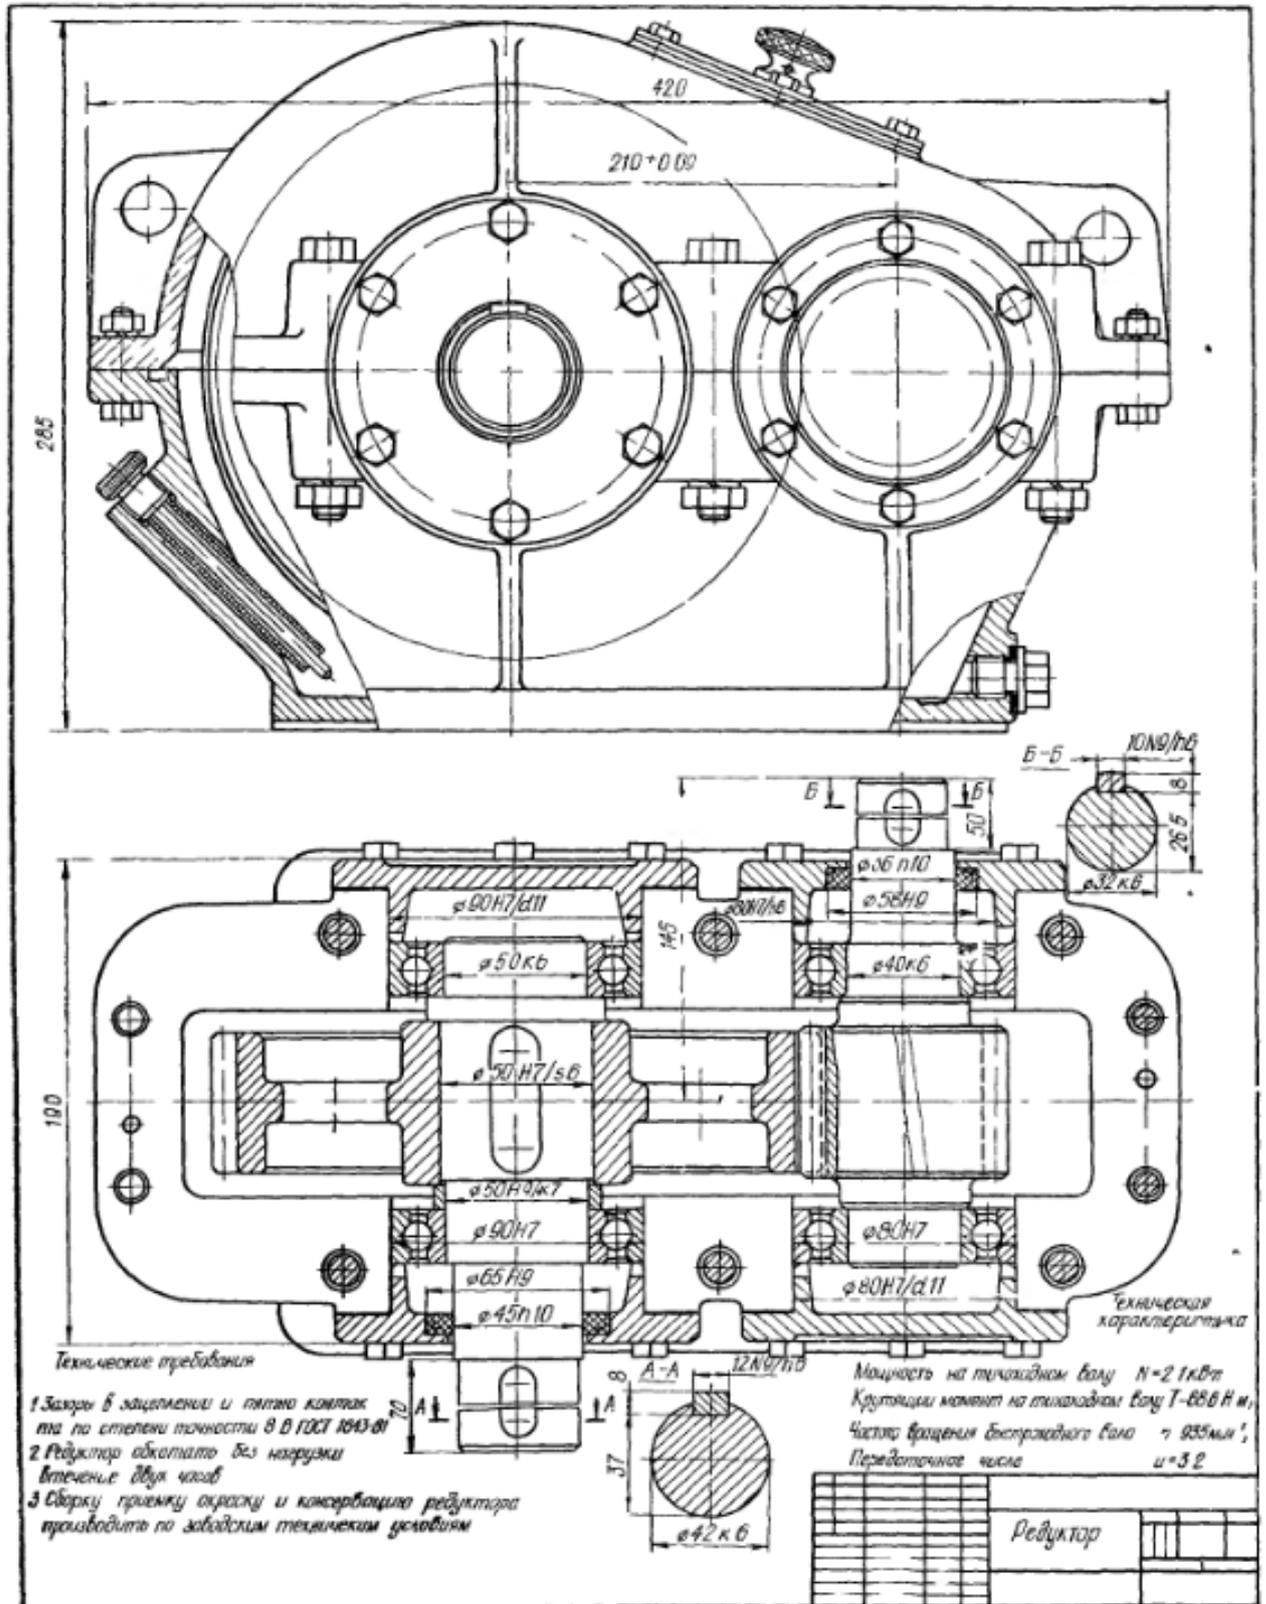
Редуктор с накладными крышками и радиальными шарикоподшипниками
